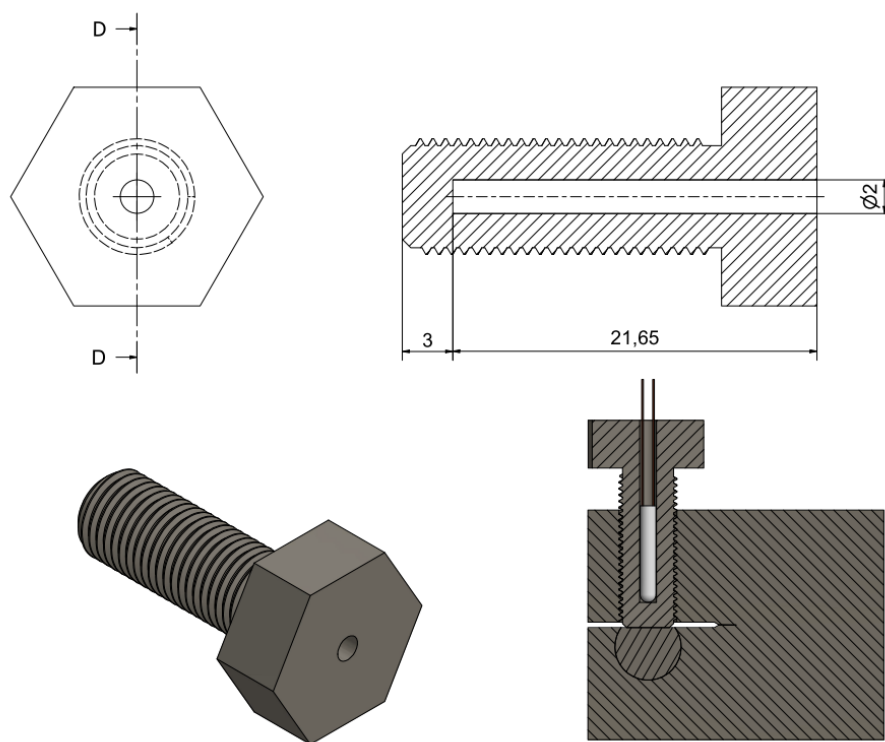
Desenhos dos componentes da primeira geometria 3D com dimensões em milímetros.
